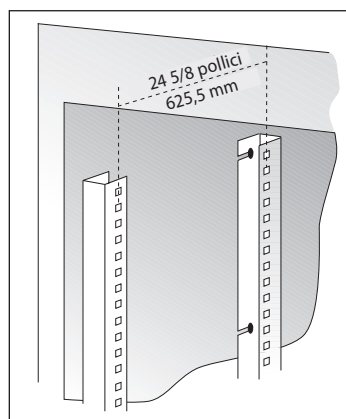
Installazione del pilastro sulla parete laterale dell'armadietto.
